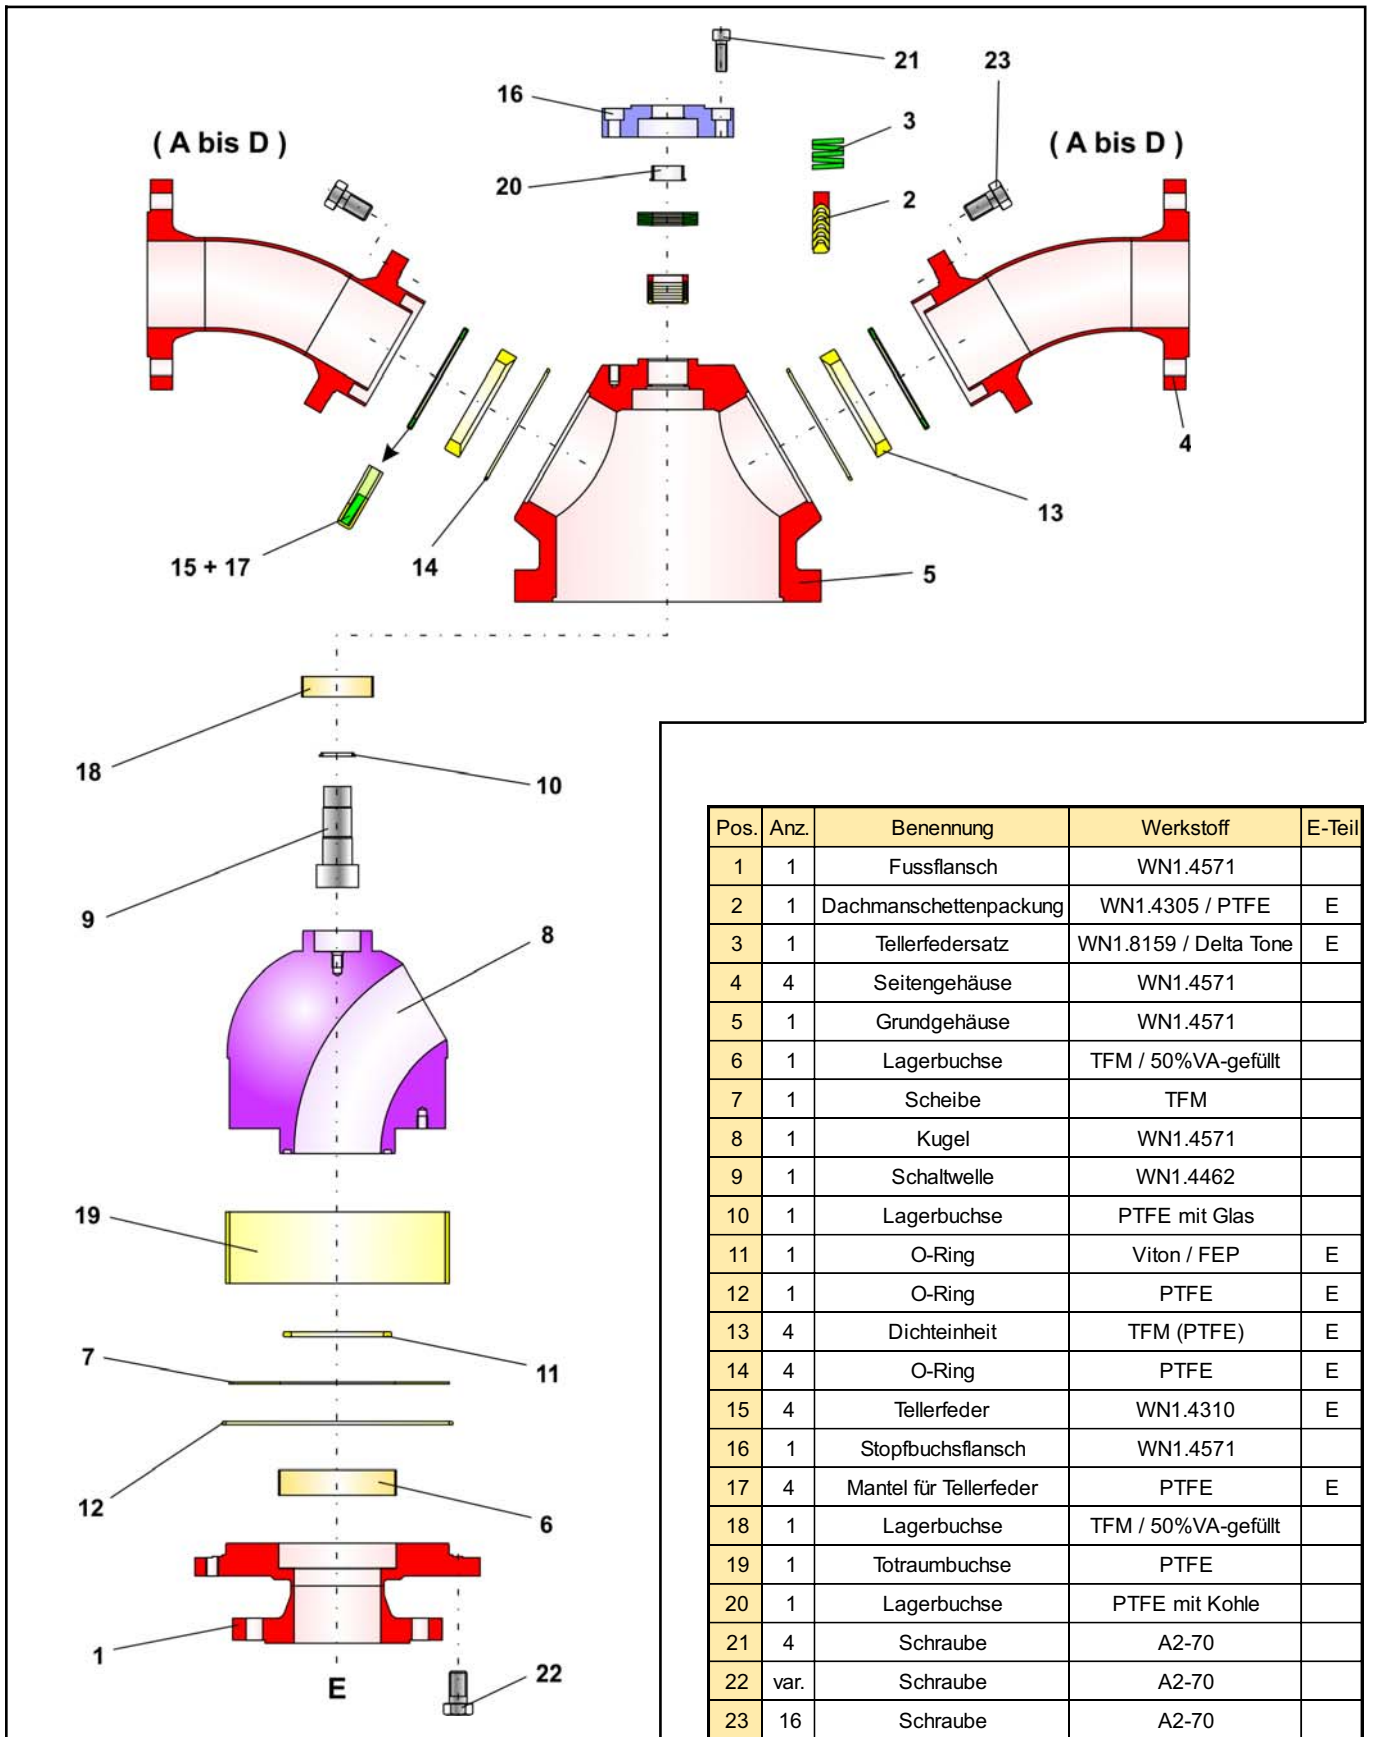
Explosionszeichnung der 3-Wege Molchweiche BR 29a
